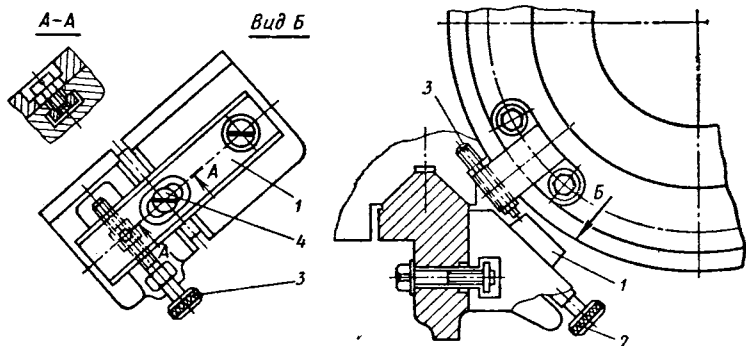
Приспособление для обработки конусов и фасонных поверхностей
